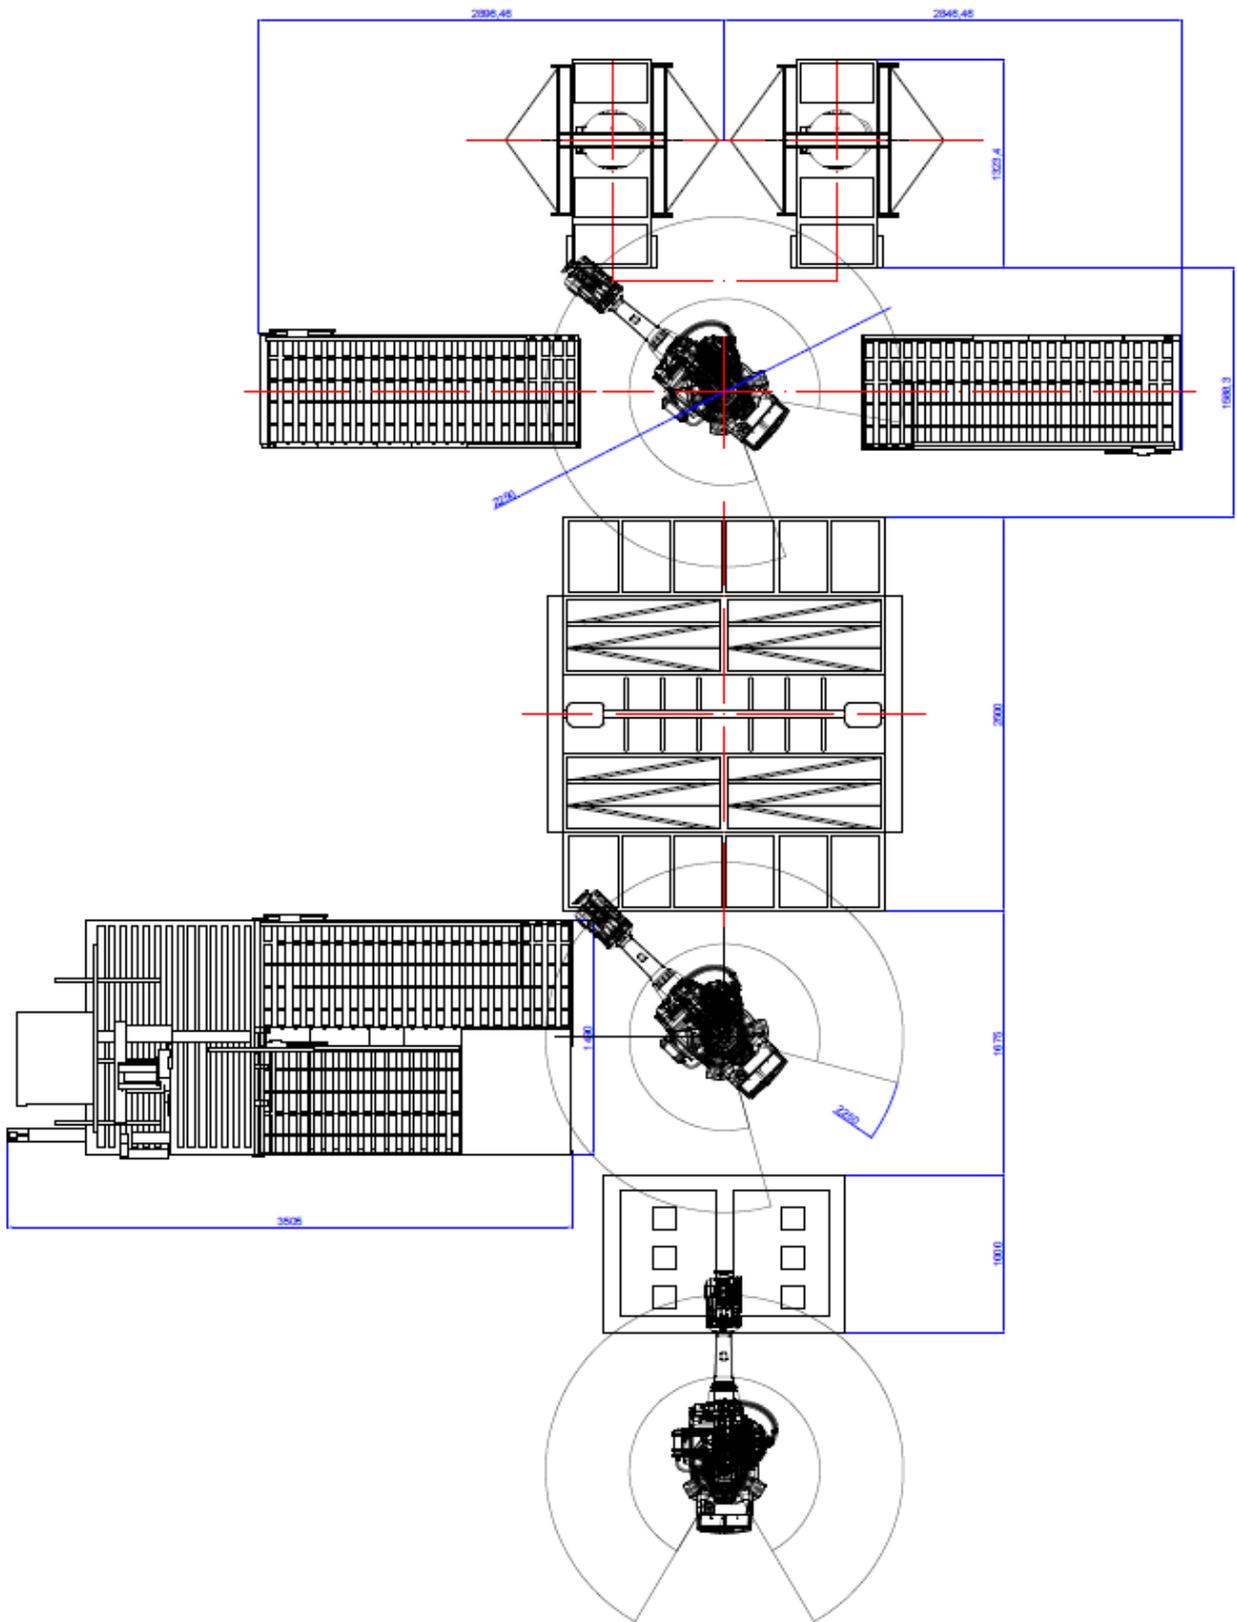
Planimetria dell'attuale linea di produzione ed assemblaggio
